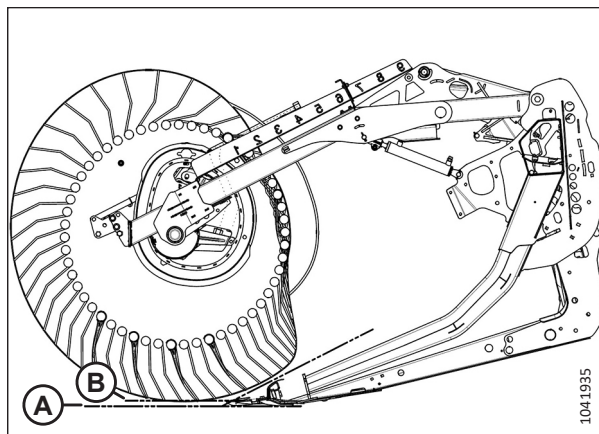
Вертикальний розріз пальця — положення ексцентрика 2
